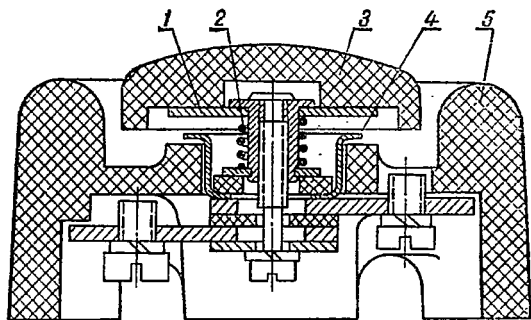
Устройство кнопочного выключателя звукового сигнала:
